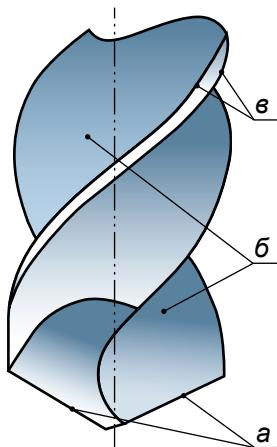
Конструкция рабочей части сверла: а – режущие кромки; б – винтовые канавки; в – спиральные ленты
